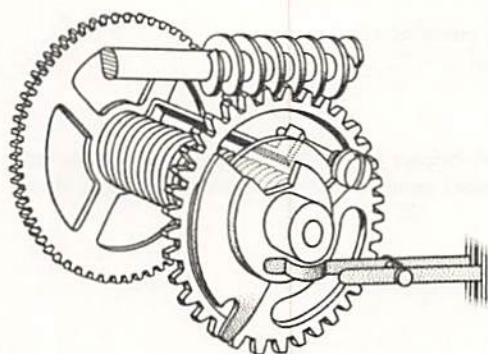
Kontaktsteuerung einer elektrischen Wohnraumuhr mit Motoraufzug
